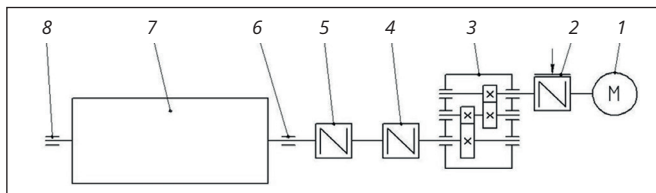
Кинематическая схема шаровой мельницы СММ2061 до модернизации: 1 – электродвигатель; 2 – муфта с тормозом; 3 – редуктор; 4, 5 – муфты зубчатые; 6, 8 – подшипниковые узлы; 7 – мельница
